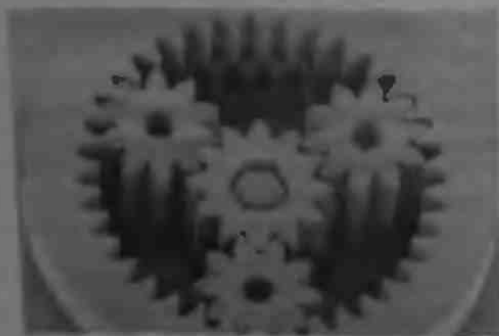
Планетарный редуктор с миниатюрными шестернями из металла. Диаметр редуктора около 1,5 мм
